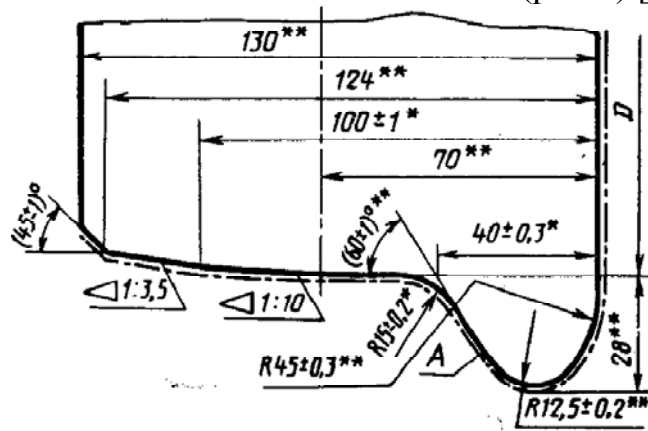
Профіль поверхні обода колеса по ГОСТ9036-88
